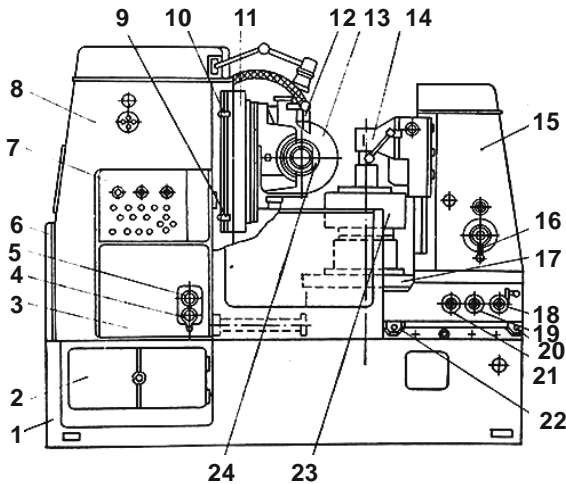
Зубофрезерний верстат 5М324А: 1 – станина; 2 – коробка швидкостей; 3 – розподільна коробка; 4 – валик ручного переміщення каретки; 5 – рукоятка автоматичного переміщення каретки; 6 – коробка поділу; 7 – пульт управління; 8 – стійка; 9, 10 – упори регулювання ходу каретки; 11 – каретка; 12 – кран охолодження; 13 – супорт; 14 – кронштейн; 15 – контрпідтримка; 16 – кран переміщення кронштейну; 17 – стіл; 18 – рукоятка встановлення упорів; 19 – гвинт переміщення столу; 20, 22 – упори підведення столу; 21 – рукоятка змащення столу; 23 – заготовка; 24 – черв'ячна фреза
